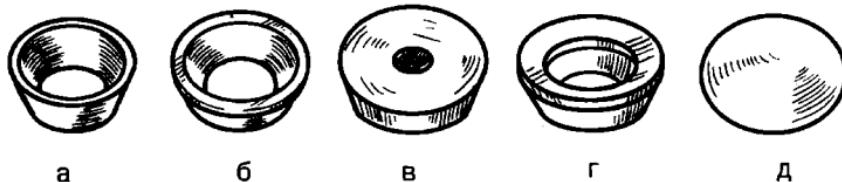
Разновидности шайб и колпачков: а — коническая шайба с заглублением; б — коническая шайба, устанавливающаяся на поверхности; в — куполообразный колпачок; г — колпачок для крестового шлица; д — резьбовой колпачок
